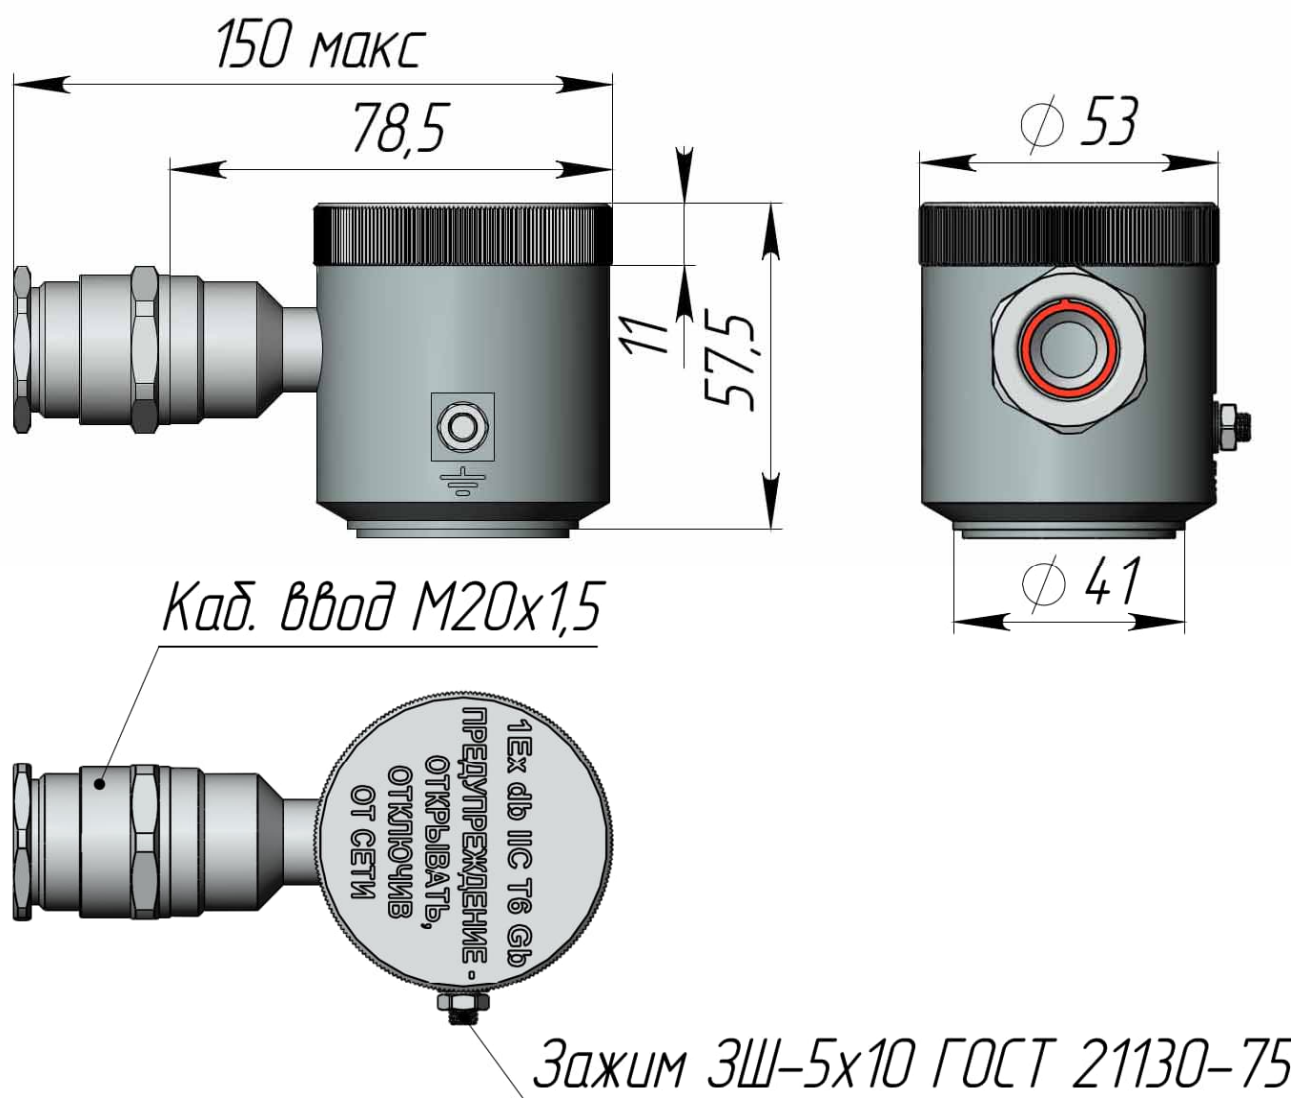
Габаритные размеры корпуса блока электронного в малом корпусе из нержавеющей стали для общепромышленного применения
